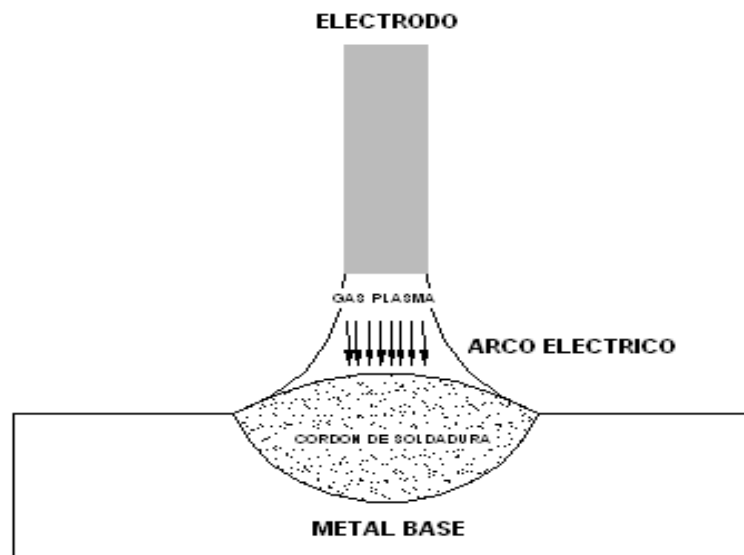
Esquema del arco eléctrico en soldadura por fusión
